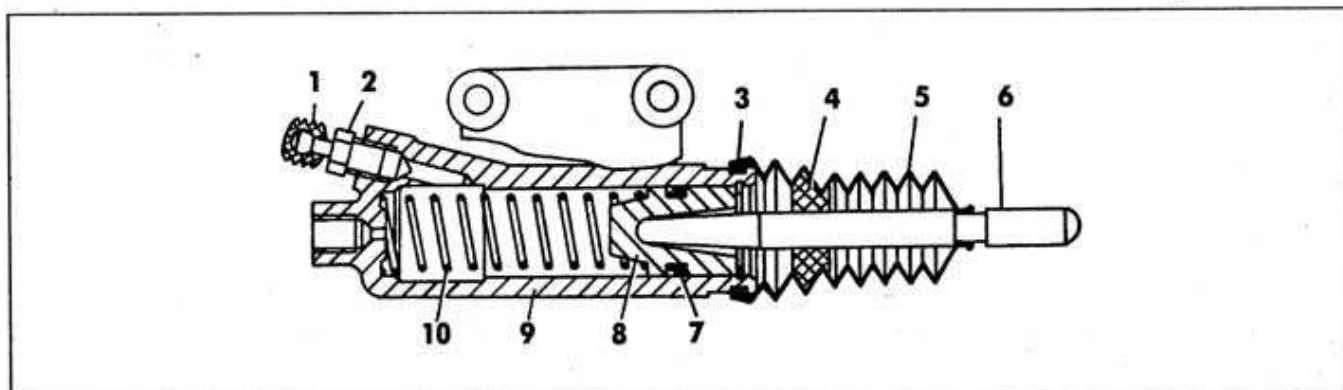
Рабочий цилиндр привода выключения сцепления:
